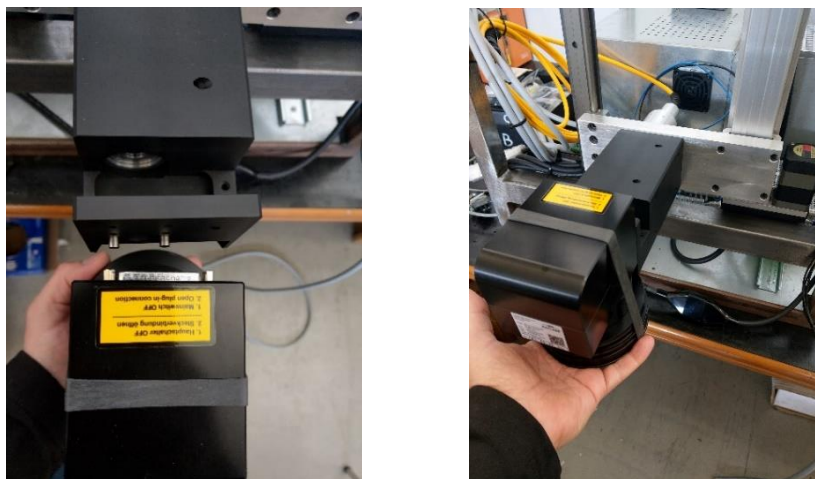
Detalhe de montagem da cabeça galvanométrica
